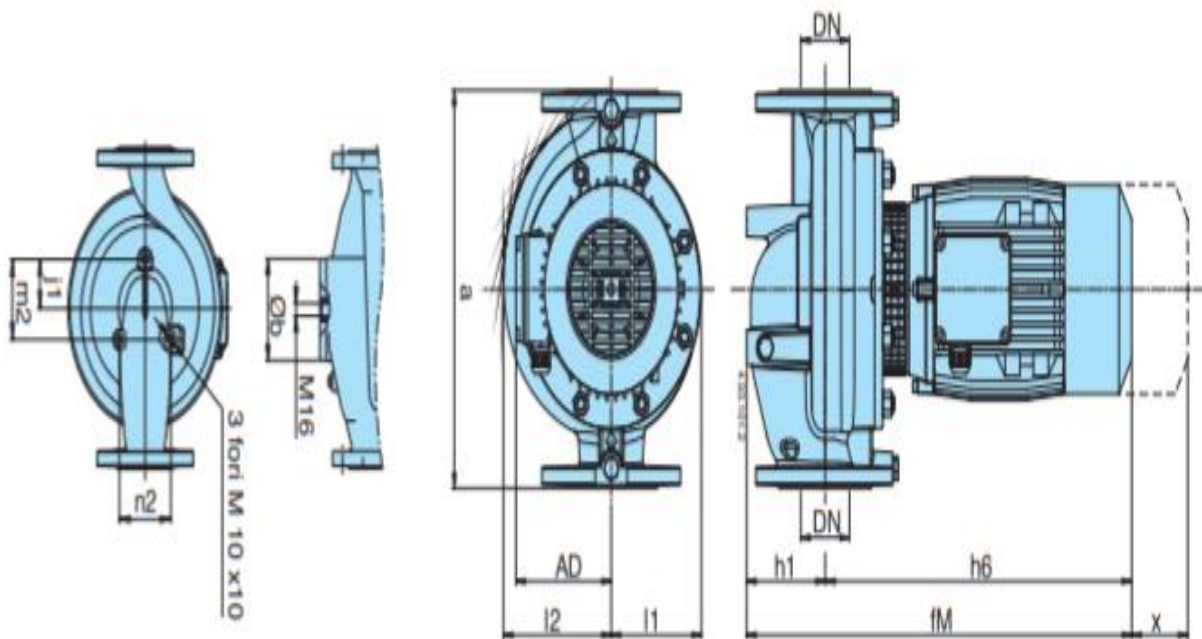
Vista de alzado, planta y perfil (Catálogo Bombas Calpeda, n.d.)
